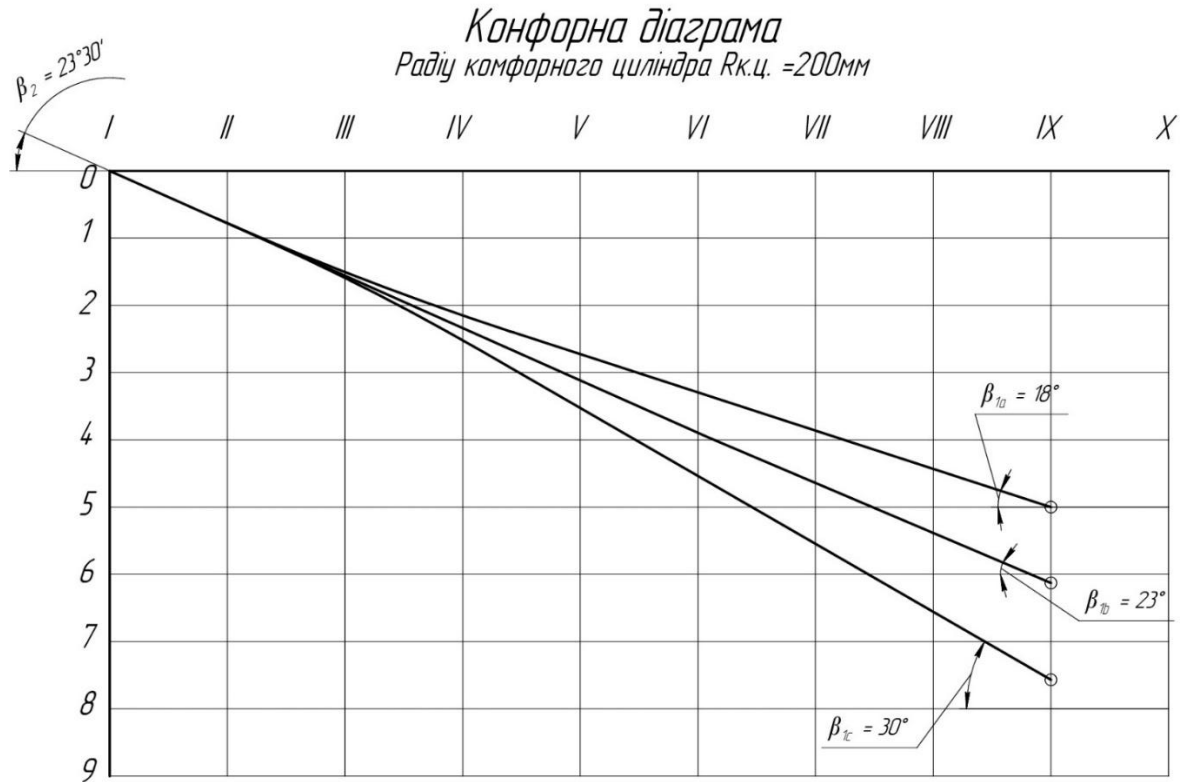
Профілювання поверхні лопаті на розгортці циліндра
